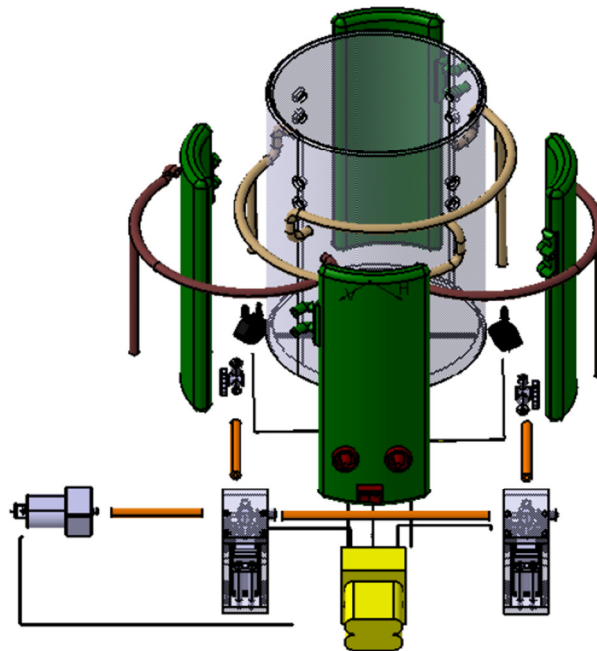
Despiece de la estructura final del sistema de autoajuste.
